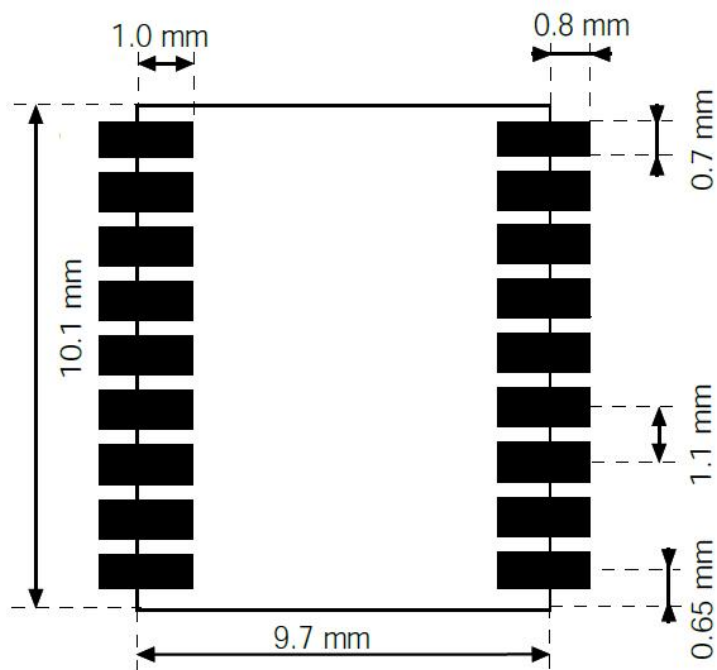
SKG09DT 封装焊盘尺寸
